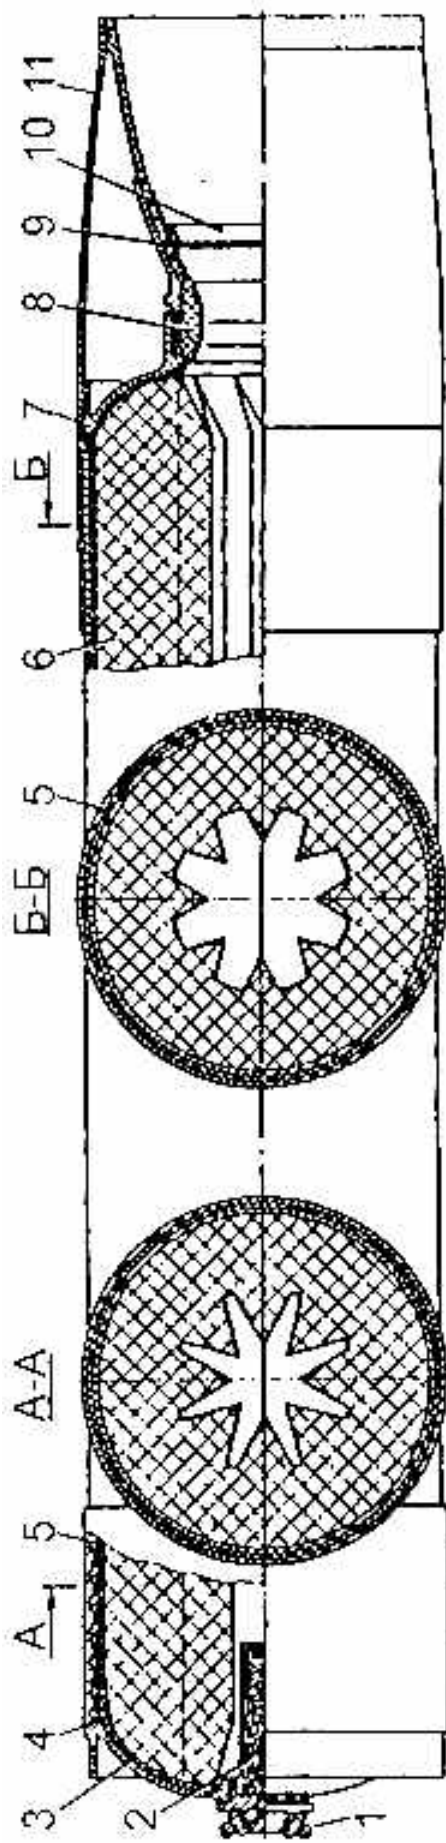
РДТП з жорсткоскріпленим зарядом: 1 — піропатрон; 2 — запалювач; 3 — ТЗП; 4 — переднє денце; 5 — текстолітова обичайка; 6 — заряд твердого палива; 7 — заднє денце; 8 — змінний вкладиш; 9 — сопловий кладиш; 10 — заглушка; 11 — кормовий обтікач
